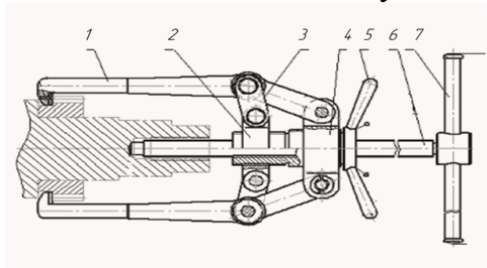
Універсальний знімач підшипників мод. LICOTA ATB-1131ATB: 1 – захват; 2 – основний корпус; 3 – упор; 4 – регульовальна голівка; 5 – регульовальна ручка; 6 – болт подачі; 7 – ручка подачі.
